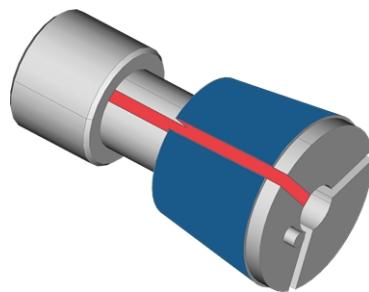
ENGRASAR LA PINZA DE SUJECIÓN; LA SUPERFICIE A LA QUE SE DEBE APlicAR GRASA APARECE MARCADA EN AZUL; LA RANURA QUE NO DEBE ENGRASARSE APARECE MARCADA EN ROJO
